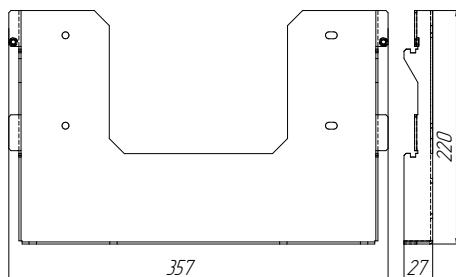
Внешний вид и габаритные размеры кронштейна для крепления ИБП Штиль SW300
